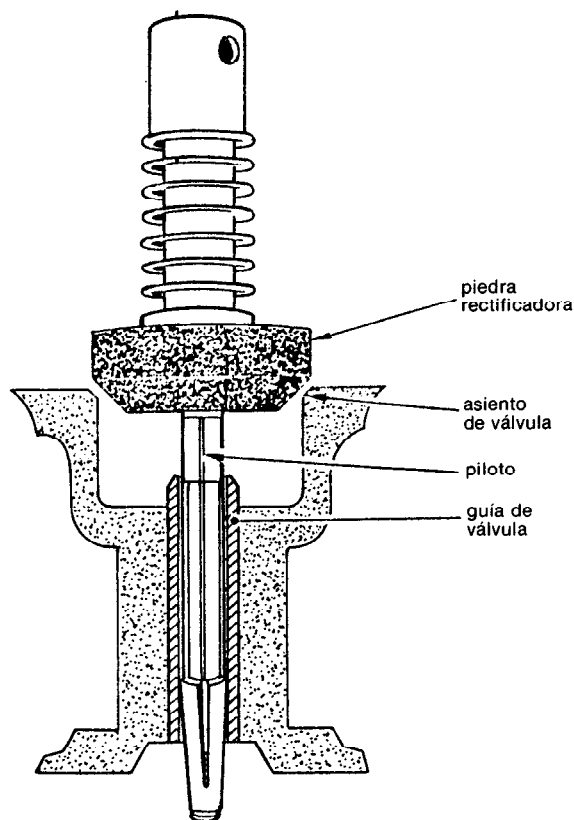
Piloto de expansión instalado en la guía de la válvula junto con la piedra rectificadora de asientos
